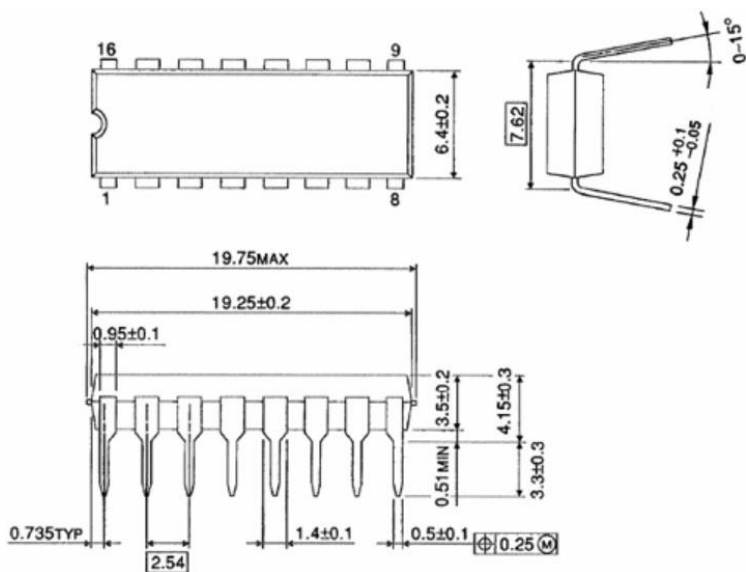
Габаритні розміри ШІМ контролера TL494L
